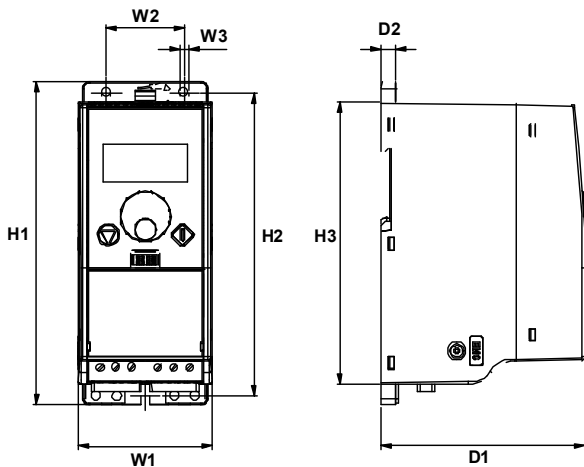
Dimensions du SmartDrive Compact, MI1-MI3
